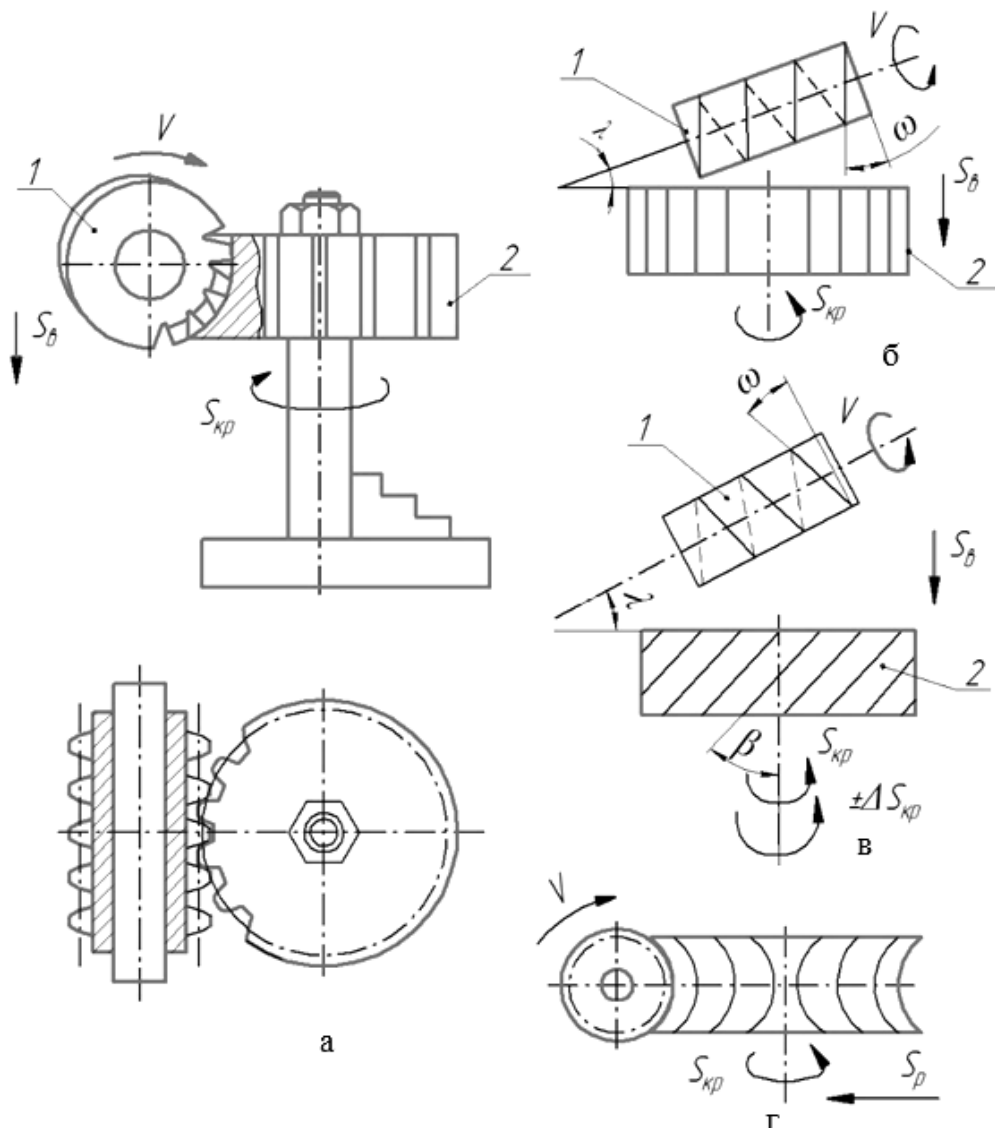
Схеми нарізування зубів на зубофрезерному верстаті
